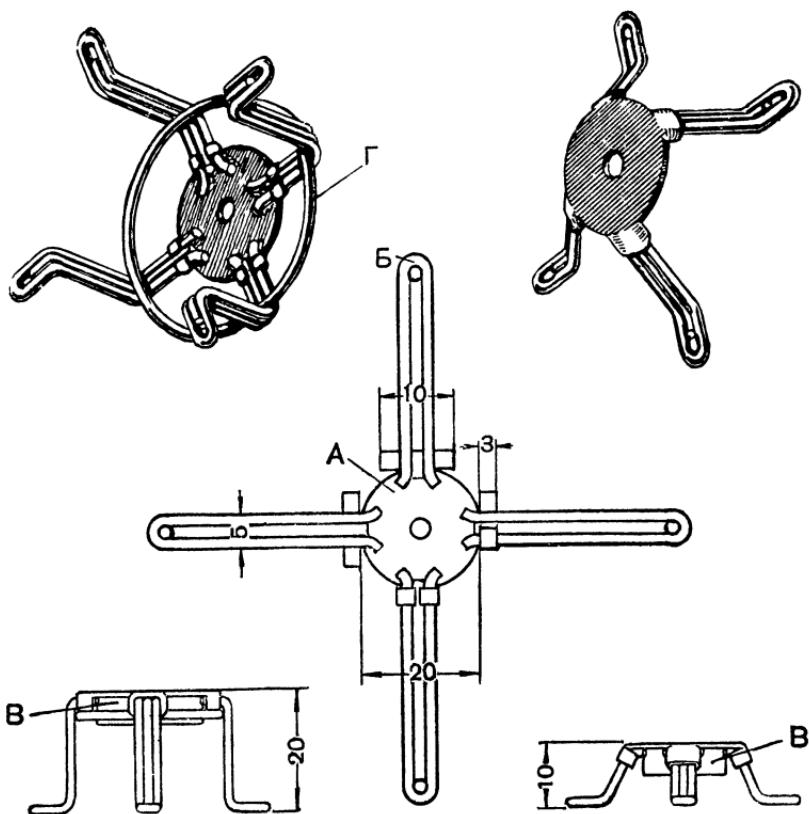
Щит для шарикоподшипников (третий вариант). В центре — схема крепления лапок; слева — передний щит; справа — задний; А — крестовина; Б — лапка; В — обойма для подшипника; Г — кольцо для щеткодержателя (см. рис. 80).
